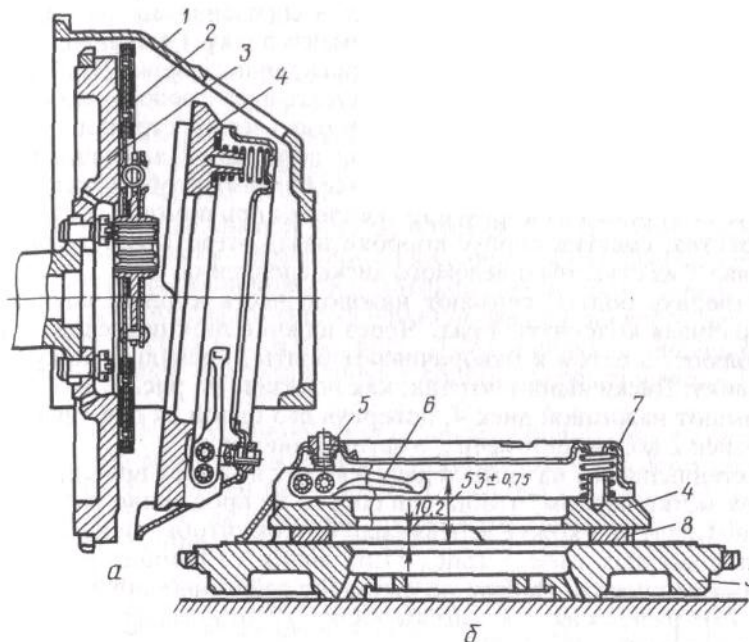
Снятие ведомого диска и кожуха (а) и регулировка сцепления (б) автомобиля ГАЗ-53А;
